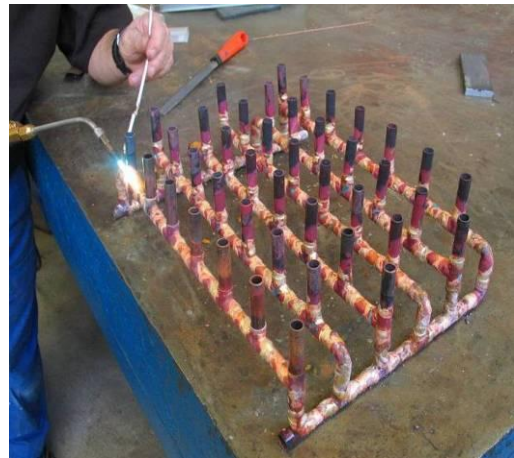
Soudage des tubes de fixation et d'assemblage sur les raccords en T et les coudes
